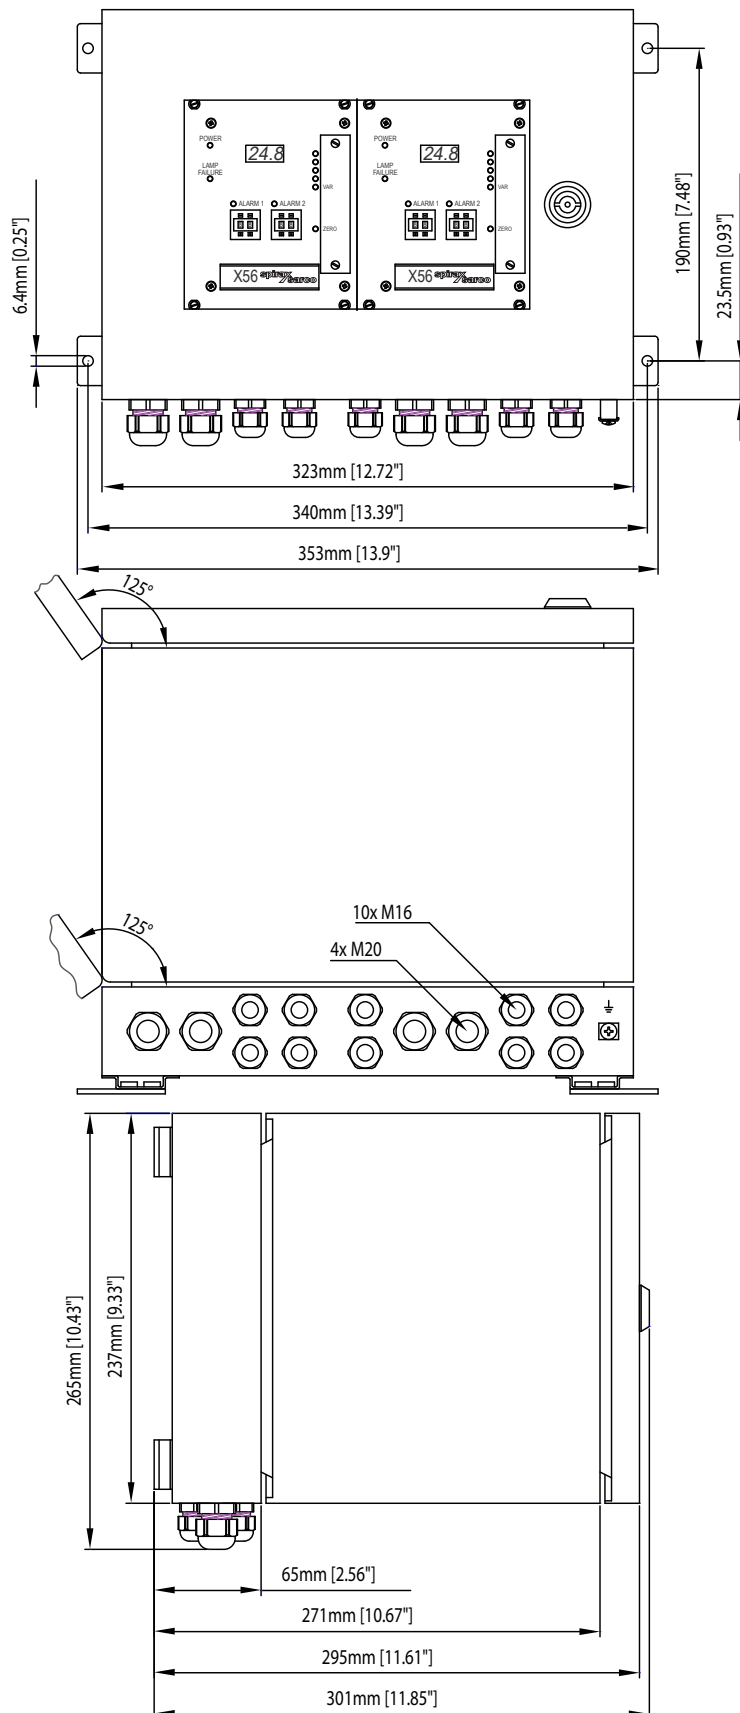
Dimensions avec boîtier B19-42 en acier inox 1.4301 / 304 - IP65 pour montage mural
